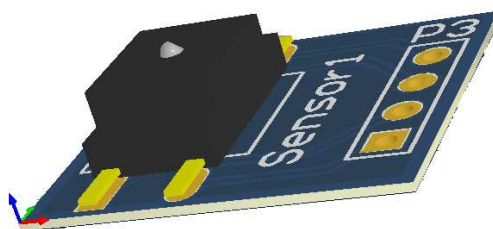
Tarjeta del sensor piezo-resistivo en 3D
